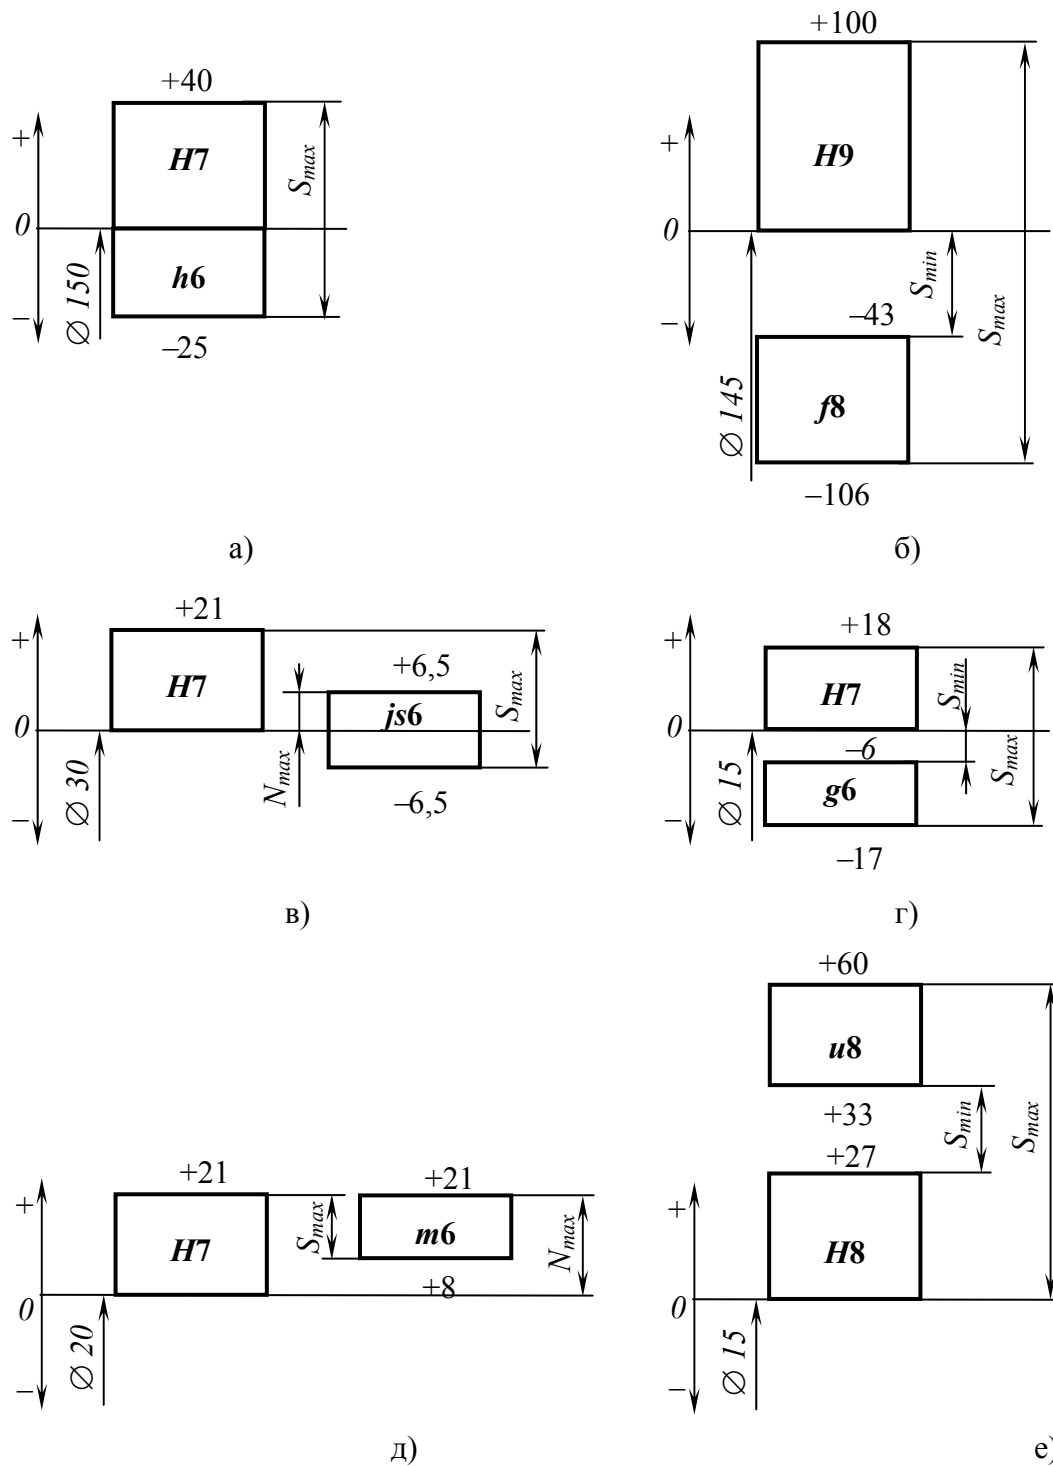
Схемы полей допусков соединений пресс-формы: а – пуансона и пуансонодержателя; б – пуансона и матрицы; в – направляющей втулки и матрицы; г – направляющей втулки и направляющей колонки; д – направляющей колонки и пуансонодержателя; е – упора и пуансонодержателя
